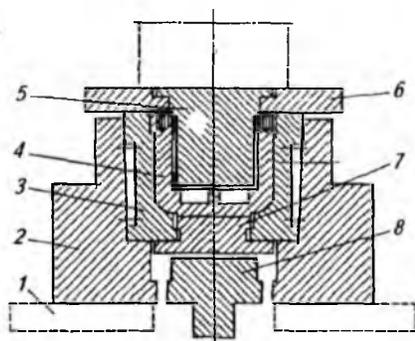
Схема пресс-формы для обжатия корпусов насосов:
